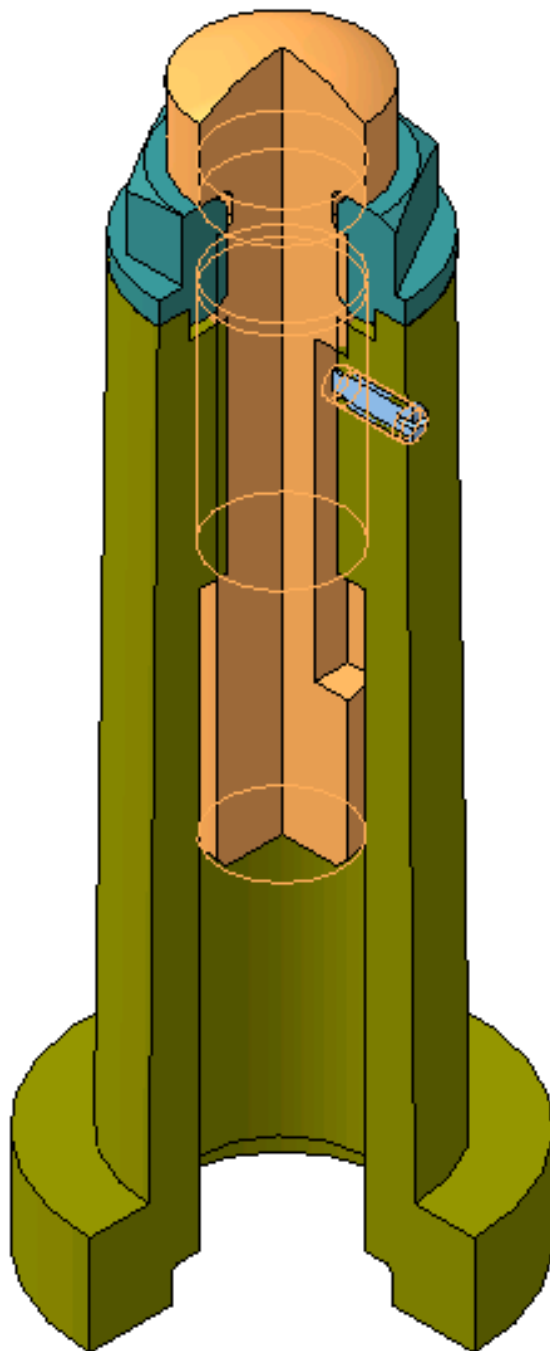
3D-модель сборки изделия «Подпорка винтовая»
